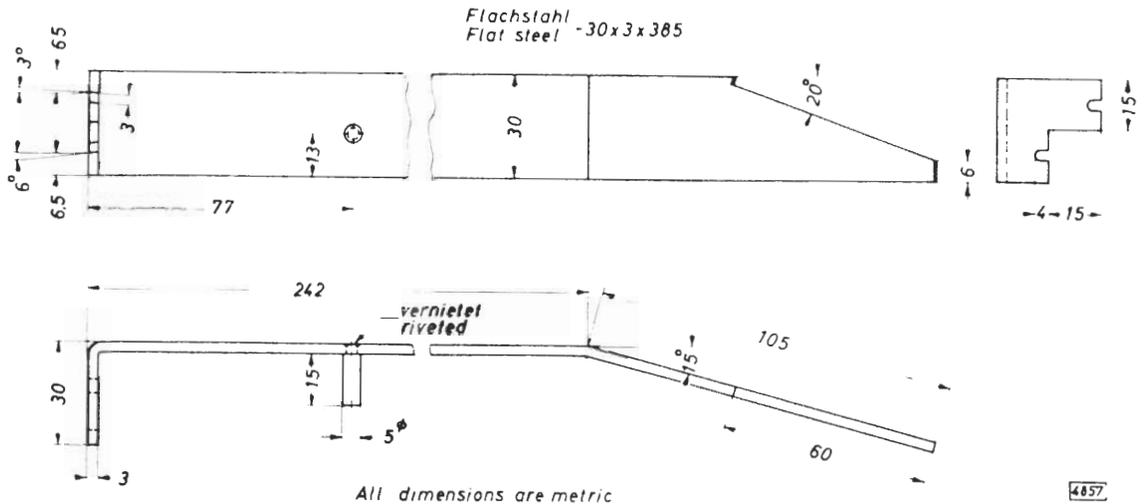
Kraftstoffmeßgerät-Prüflehre für Kadett-Typen
